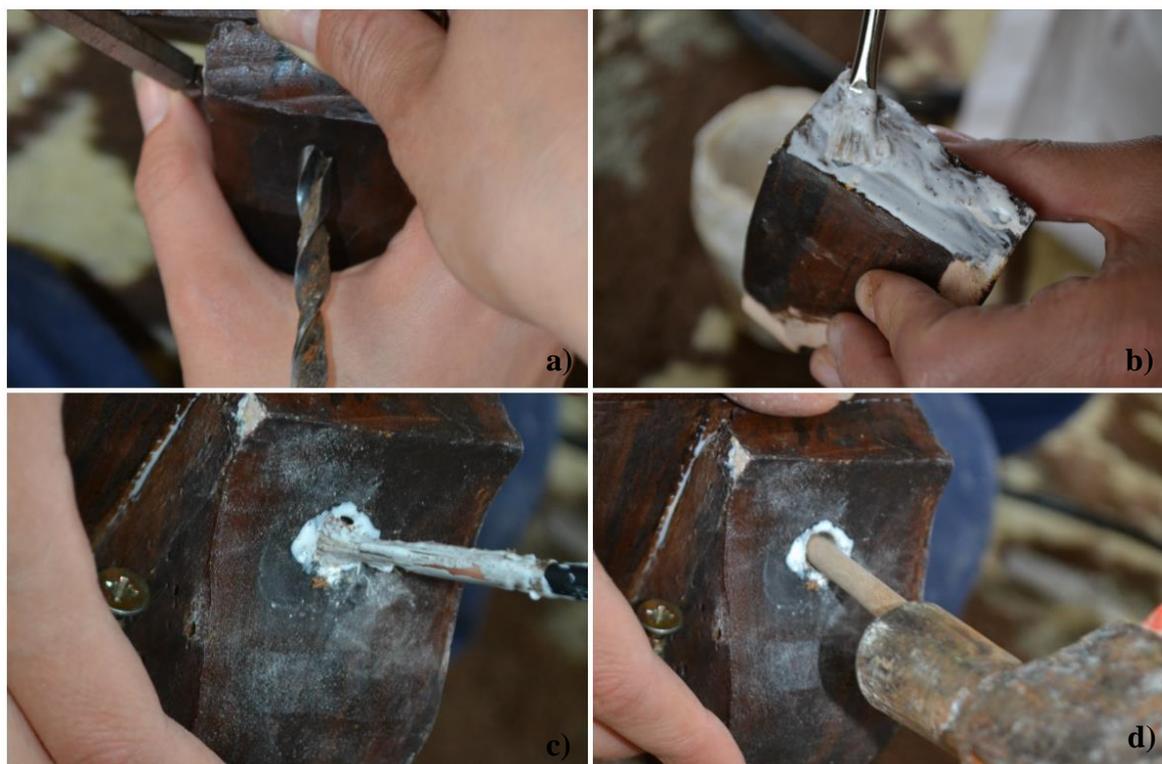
Colagem de peças travada por cavilhas de madeira: a) perfuração das peças para introdução de cavilhas; b) aplicação de cola nas áreas de colagem; c) Introdução de cola no orifício de ligação; d) introdução da cavilha de reforço da colagem. Fonte: de elaboração própria.
